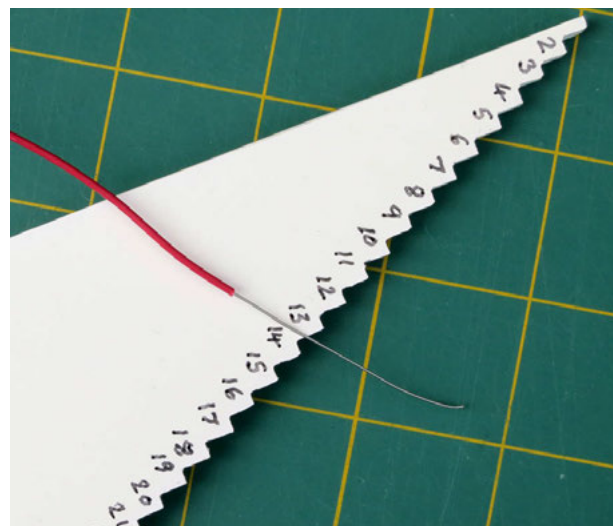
Calibre fait maison pour plier et trier les fils utilisés sur les plaques d'essai (gradué en pas de 2,54 mm).
